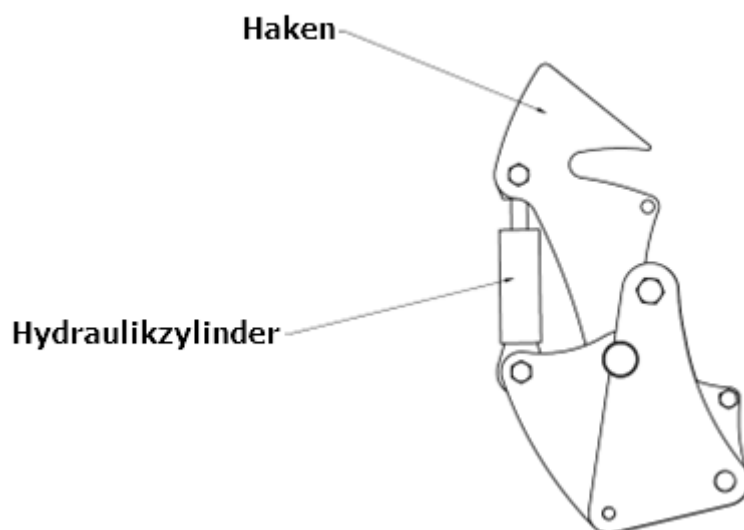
Hydraulische Maschinenflügelverriegelung.
